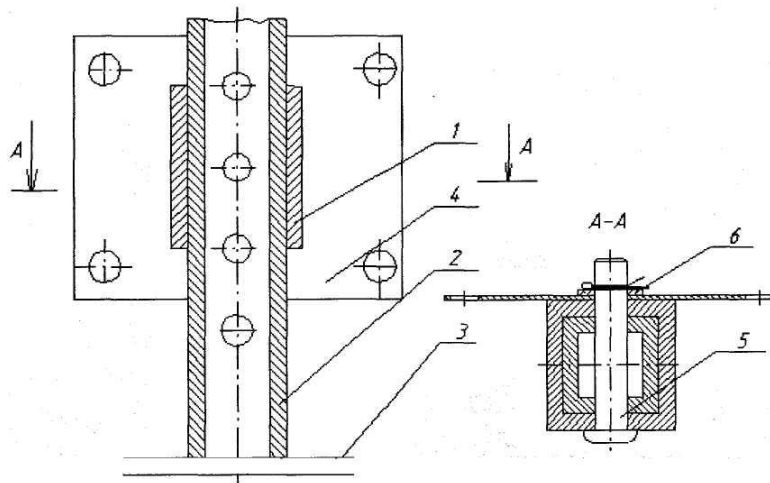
Опора агрегату для передпосівного обробітку ґрунту: 1 – тримач; 2 – стояк; 3 – пластина; 4 – кріпильна пластина; 5 – палець; 6 – шайба.
